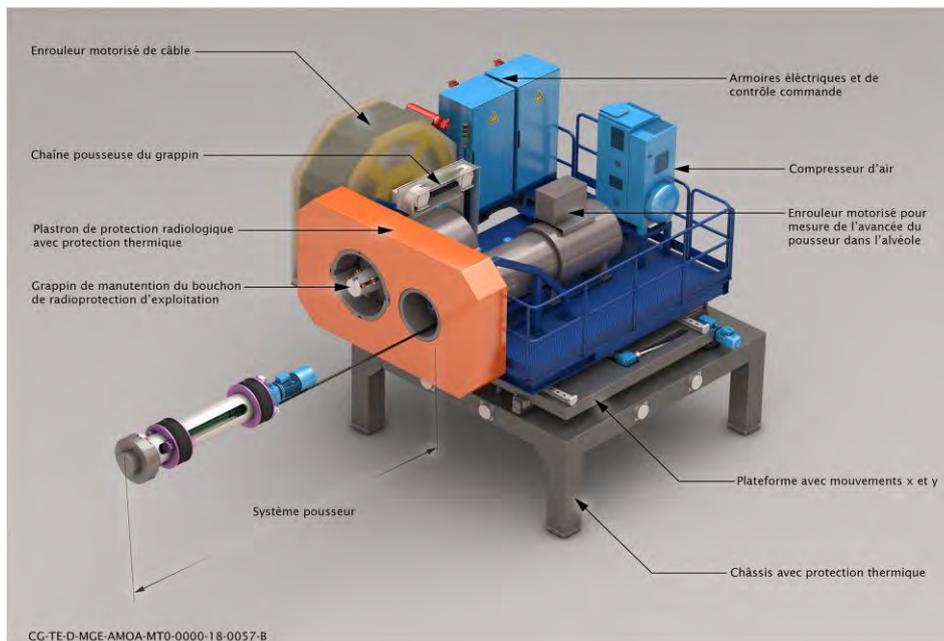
Illustration du robot pousseur des colis de stockage HA
